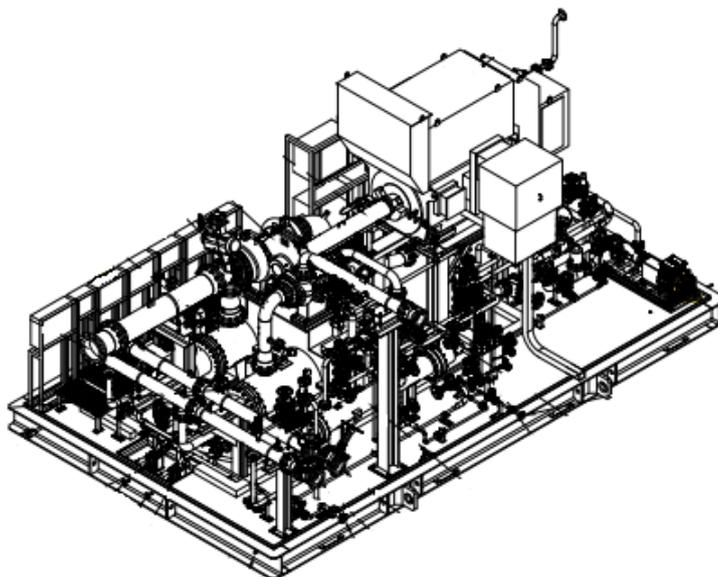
Воздушный центробежный компрессор со встроенным редуктором компании Hanwha Power System модель SE-32A/3
